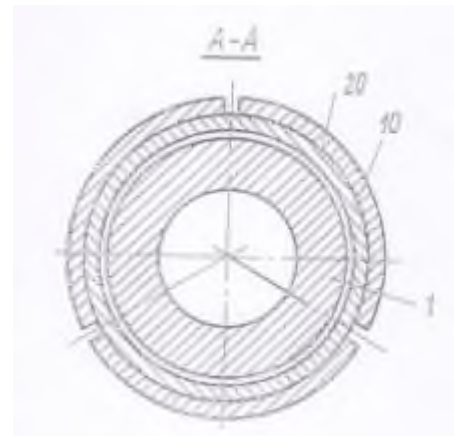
Інструмент для обробки глибоких отворів, розріз А-А
